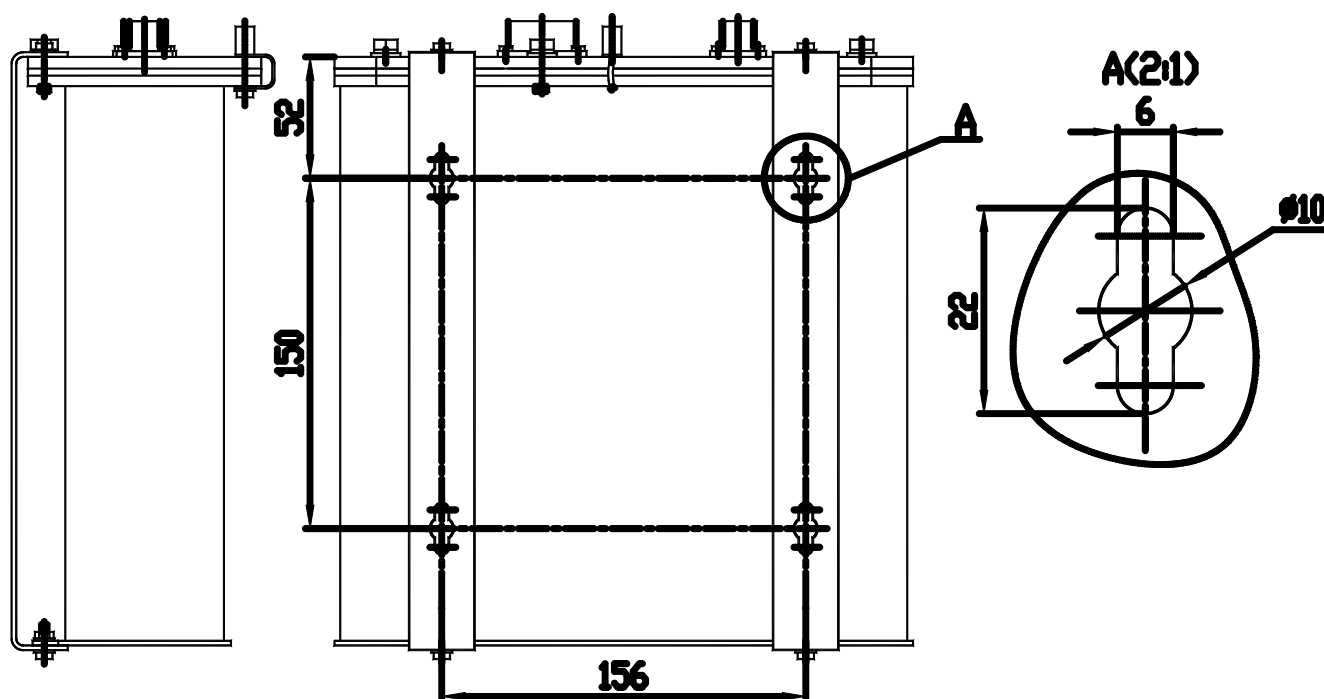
Разметка стены для установки блока в герметичном корпусе.
